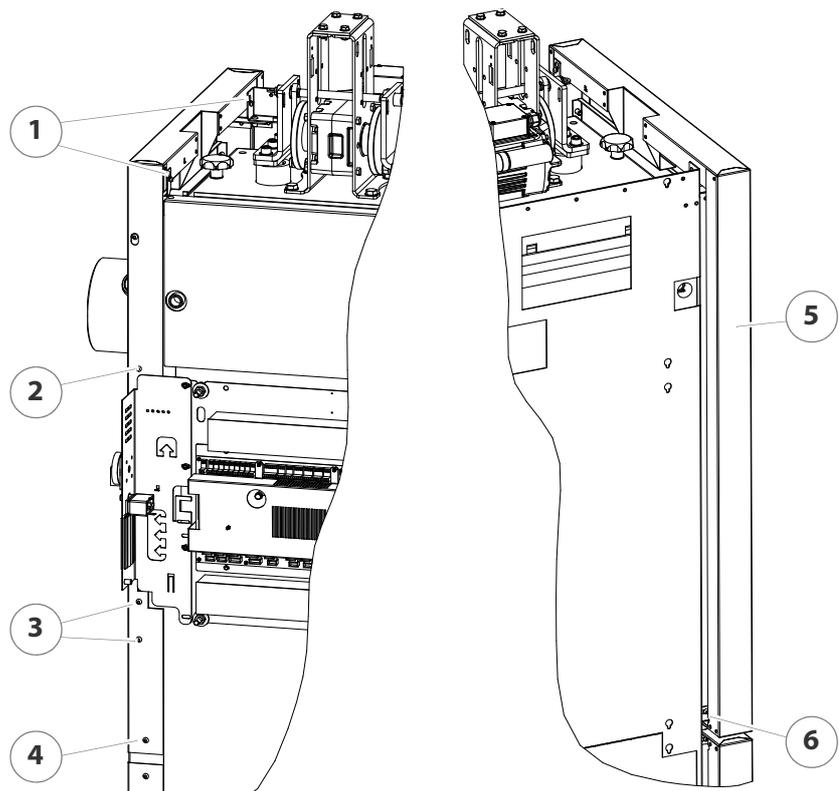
/39 - Montage des jaquettes latéral côté conduit de fumée, en haut
